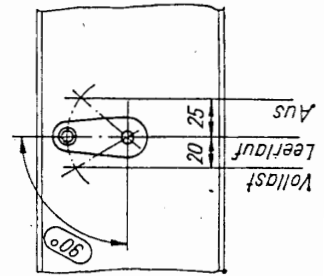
Fahrregler-, Gestänge- und Fahrfußbelanbau
